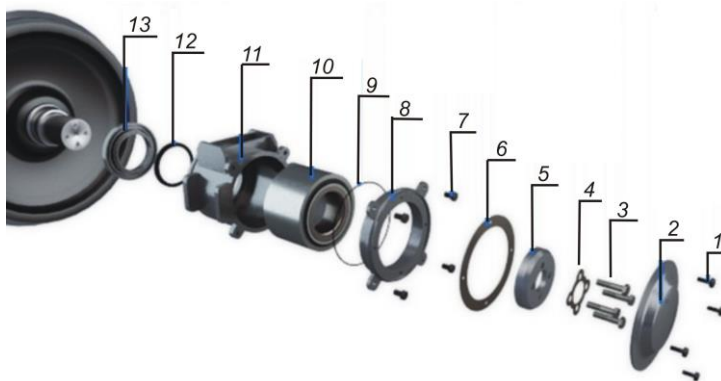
К монтажу корпусного конического подшипникового узла:
